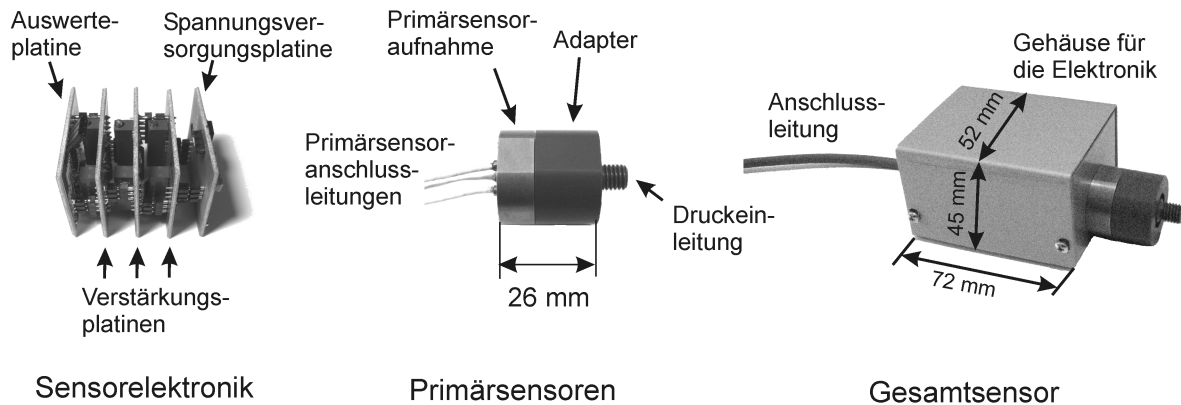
Ansichten des redundanten Drucksensors und seiner Baugruppen
